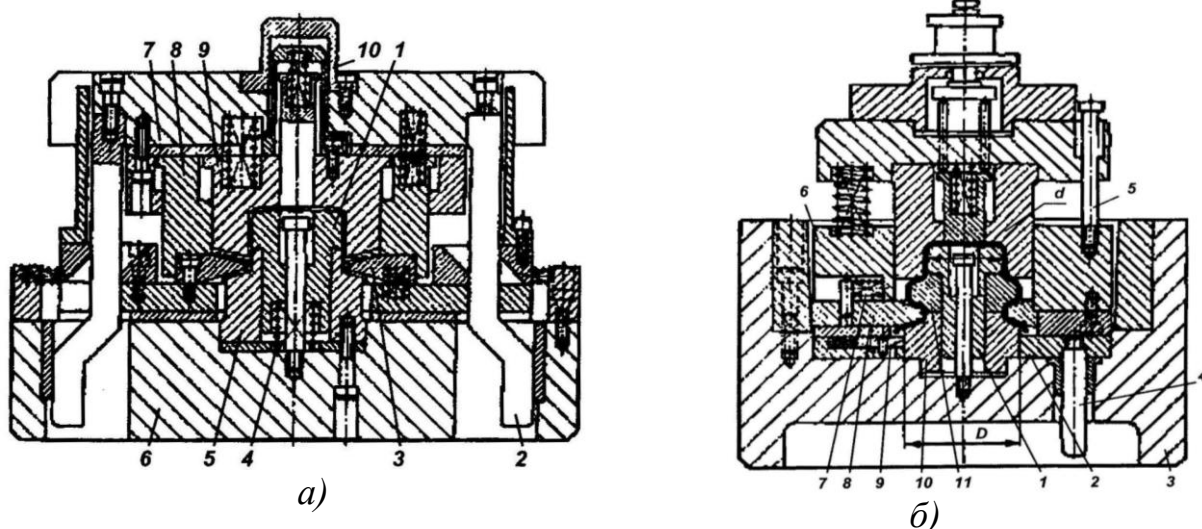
Штampi для формування шківа вентилятора: а) остаточного; б) попереднього
